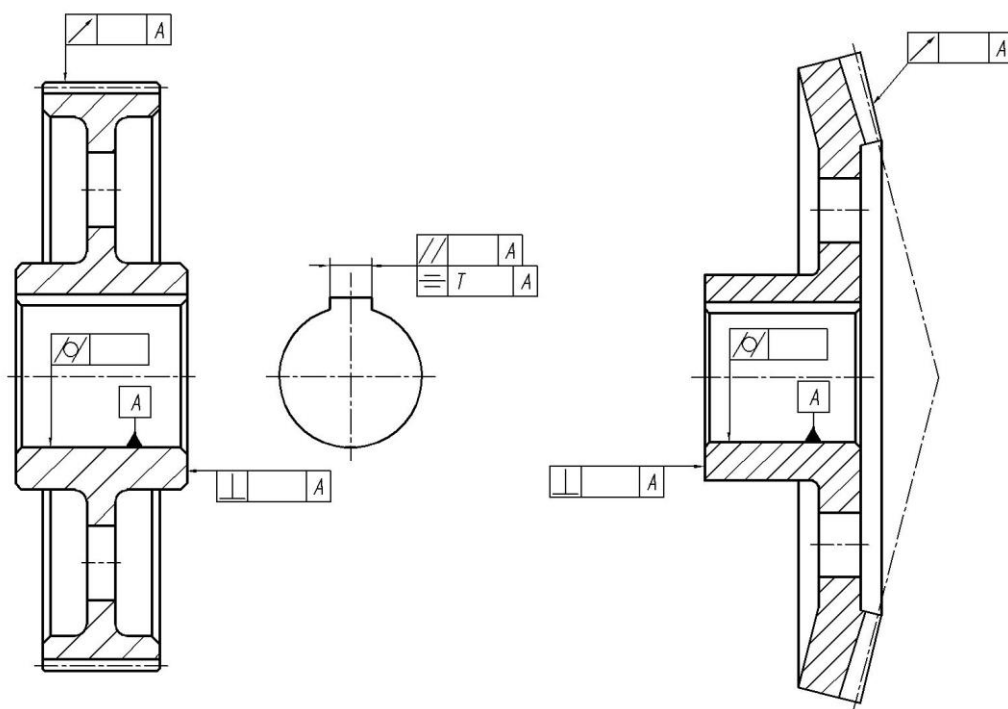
Размещение обозначений допусков форм и расположения поверхностей на чертежах зубчатых колес
